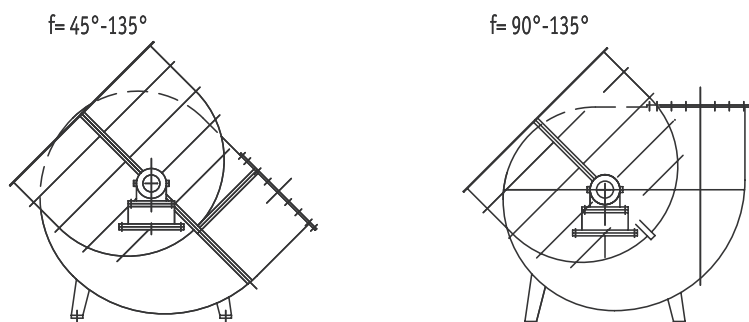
Положение корпуса тягодутьевых машин типа Д (ЛЕВ).
